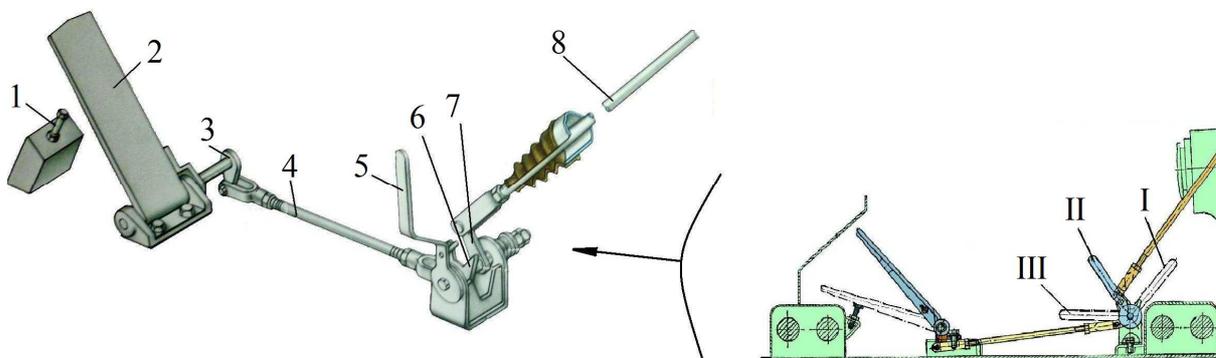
Устройство для открытия крышки кожуха вентилятора
